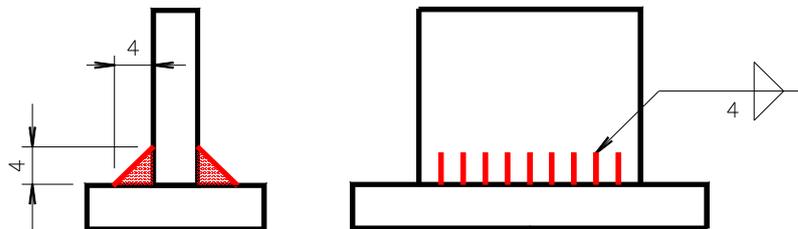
representação do cordão de solda com ângulo de 45° .
